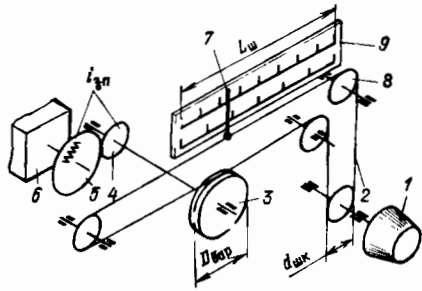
Кинематическая схема механизма настройки с гибкой связью и зубчатыми колесами: 1 — ручки настройки; 2 — гибкая связь; 3 — барабан; 4, 5 — зубчатые колеса; 6 — исполнительный элемент; 7 — указатель; 8 — направляющие стойки; 9 — шкала
